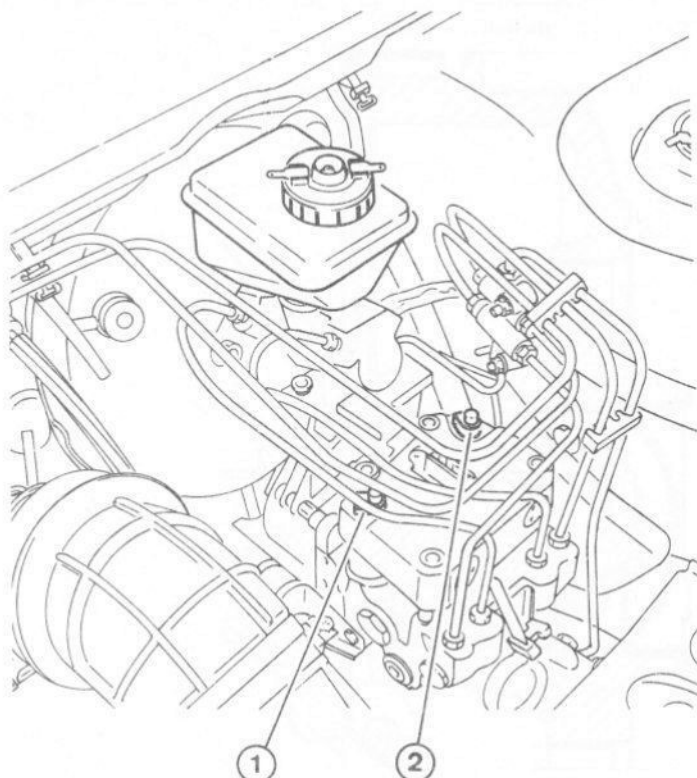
Vis de purge (1 et 2) sur le régulateur ABR (Sec 18)
